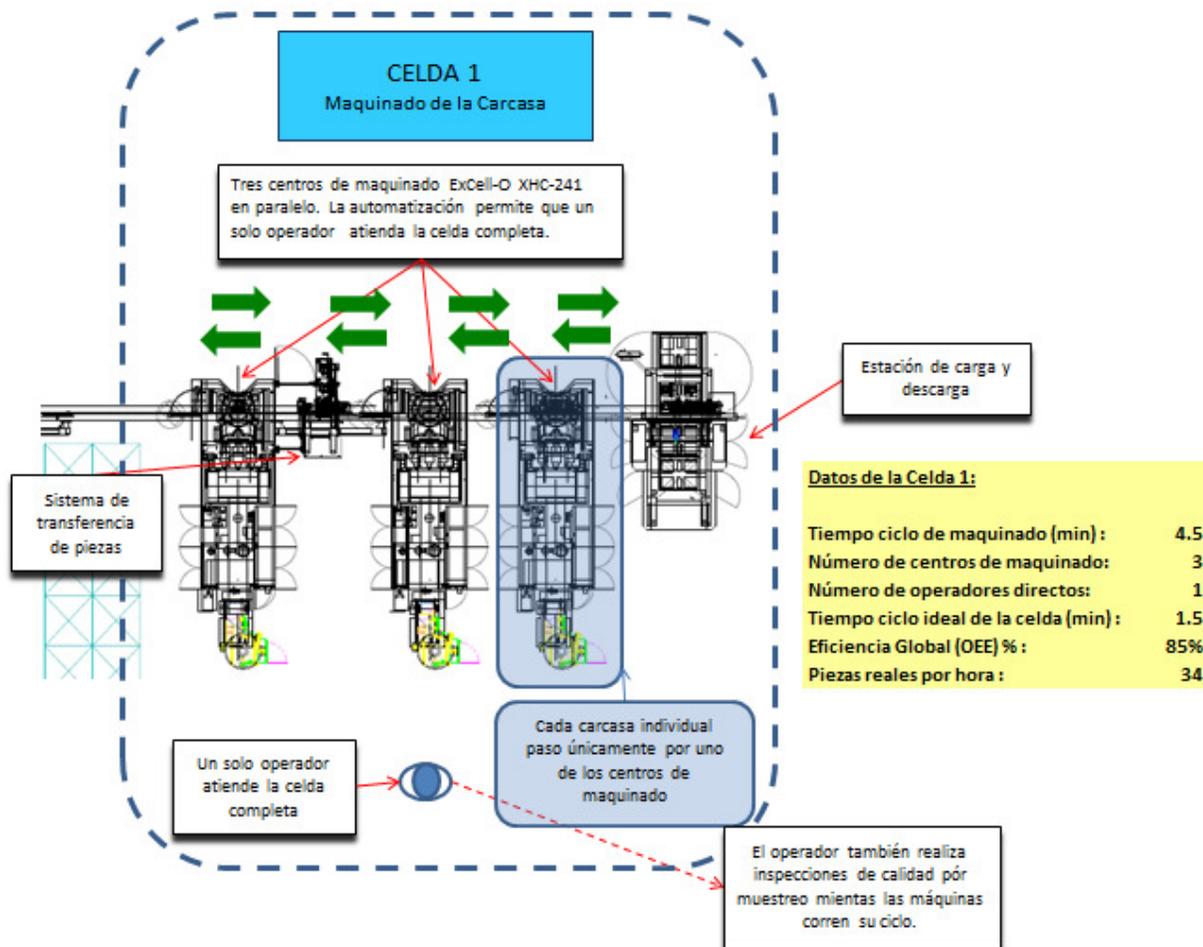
Configuración o layout de la celda de maquinado de la carcasa.
